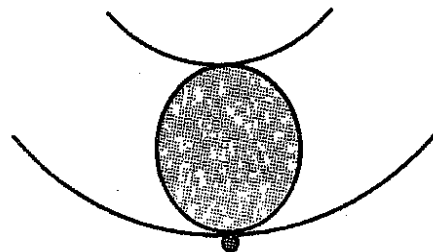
Esquema de bola de rodamiento sobre defecto en pista externa
